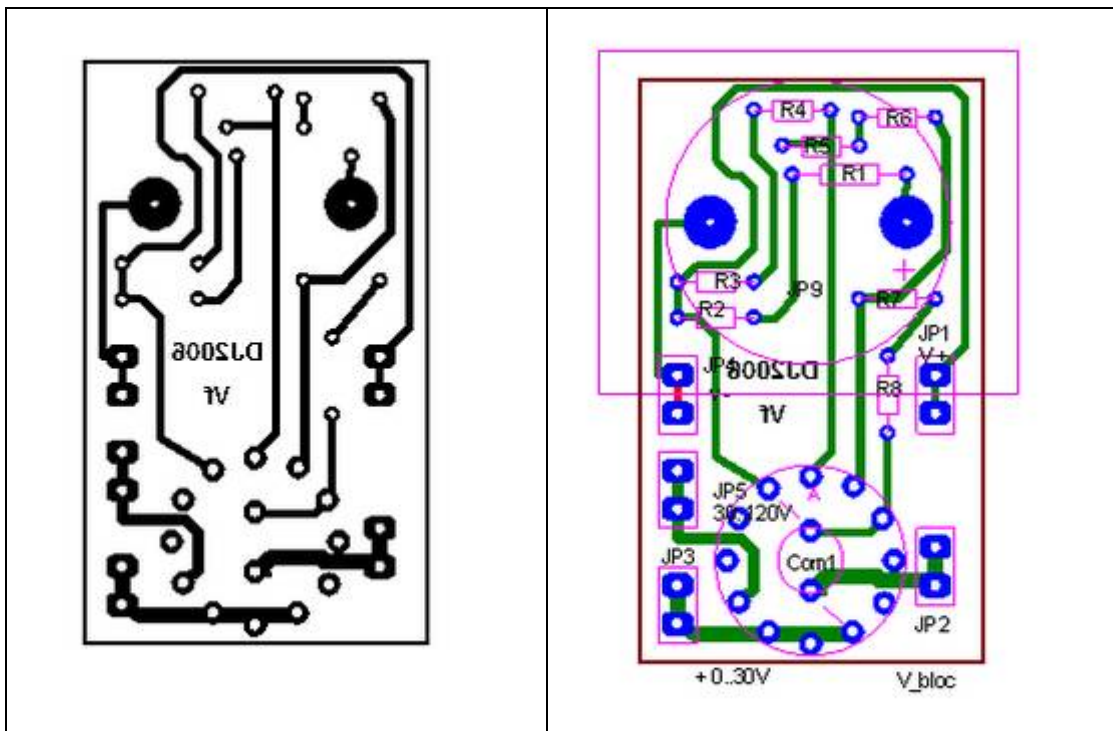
PCB mesure tension Vf et implantation des résistances.
